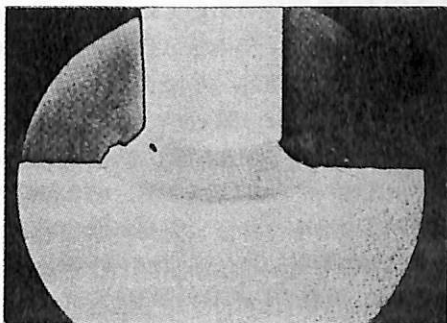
ASTM 304L steel bolts stud welded to ABS-CS steel⁷⁾
